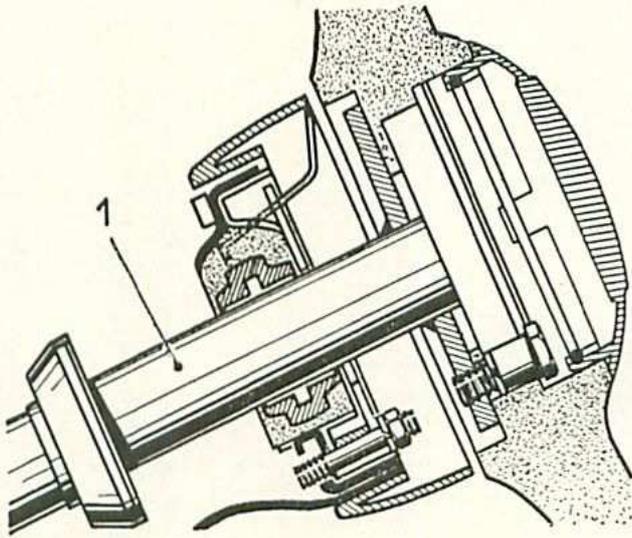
Vue en coupe de la partie supérieure du tube de direction équipé.
